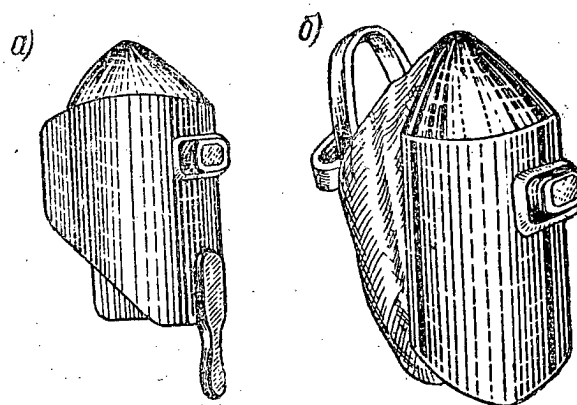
Приспособление для защиты глаз сварщика:
